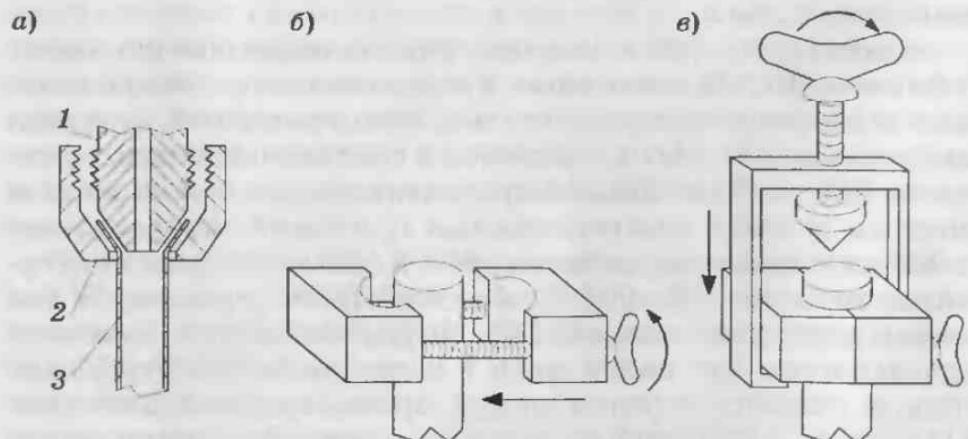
Схема бортования: а — схема штуцерного соединения (1 — ниппель; 2 — накидная гайка; 3 — штуцер, медная труба); б — схема закрепления медной трубы в бортовке; в — схема подачи конуса для бортовки трубы
